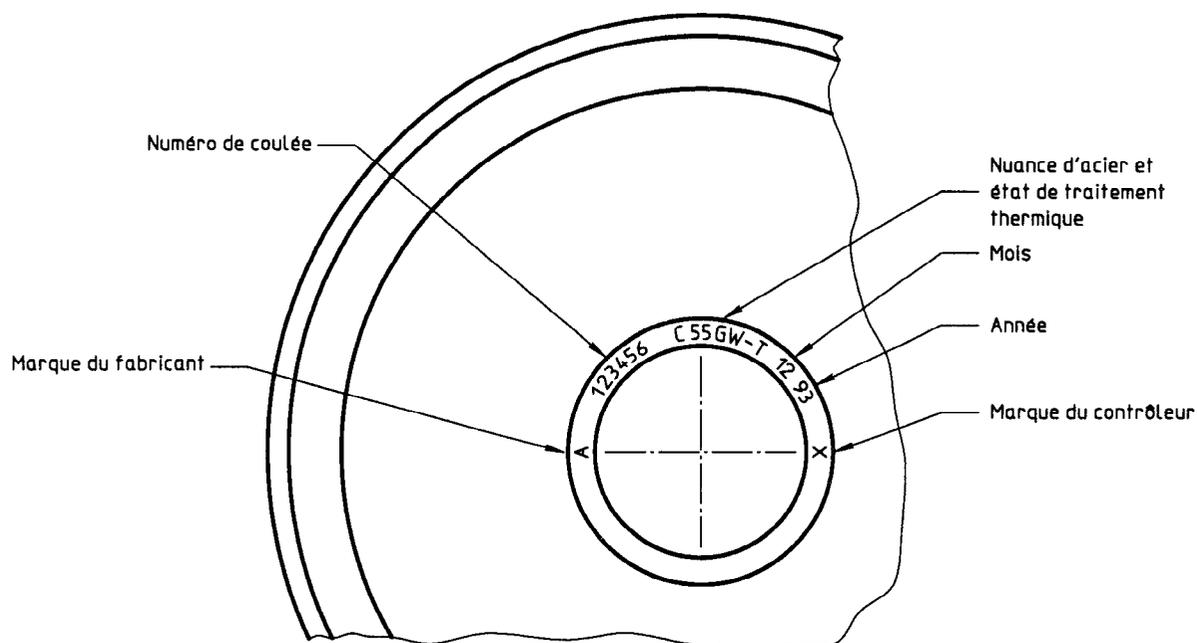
Exemple de marquage par estampage des roues laminées, forgées ou moulées (voir 5.6)
